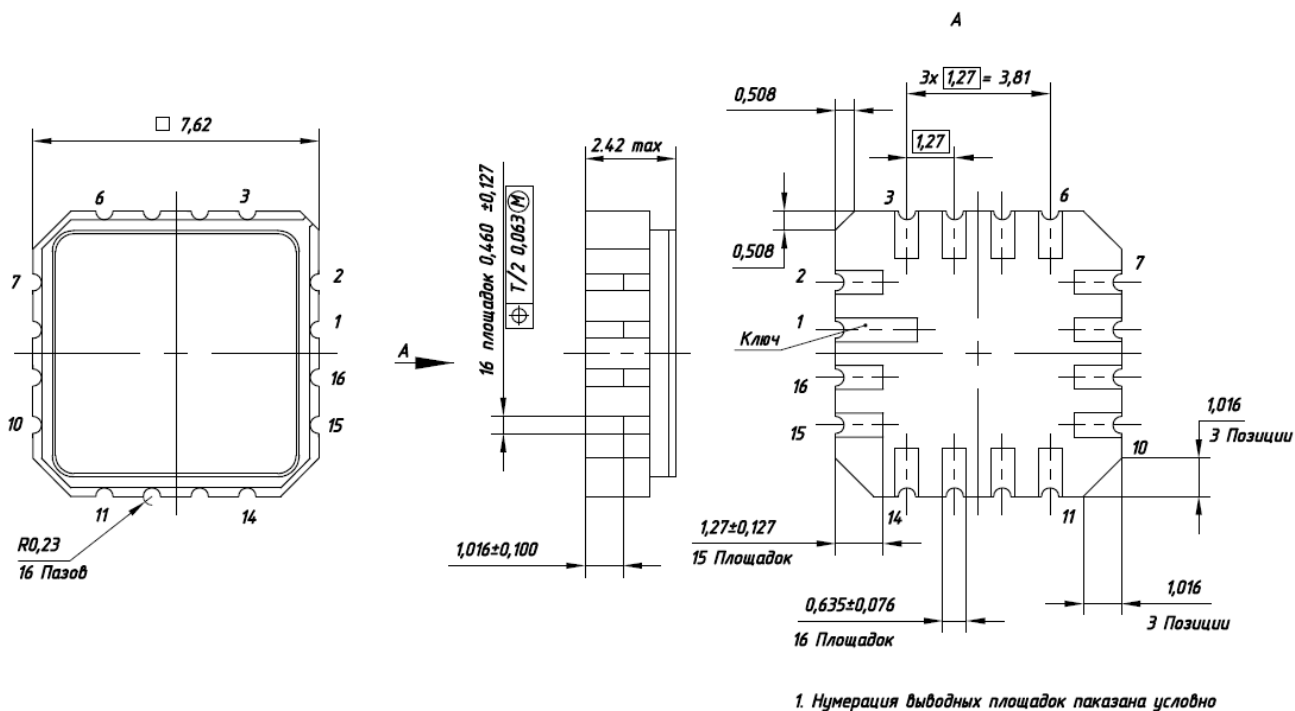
Габаритный чертеж корпуса 5119.16-А
